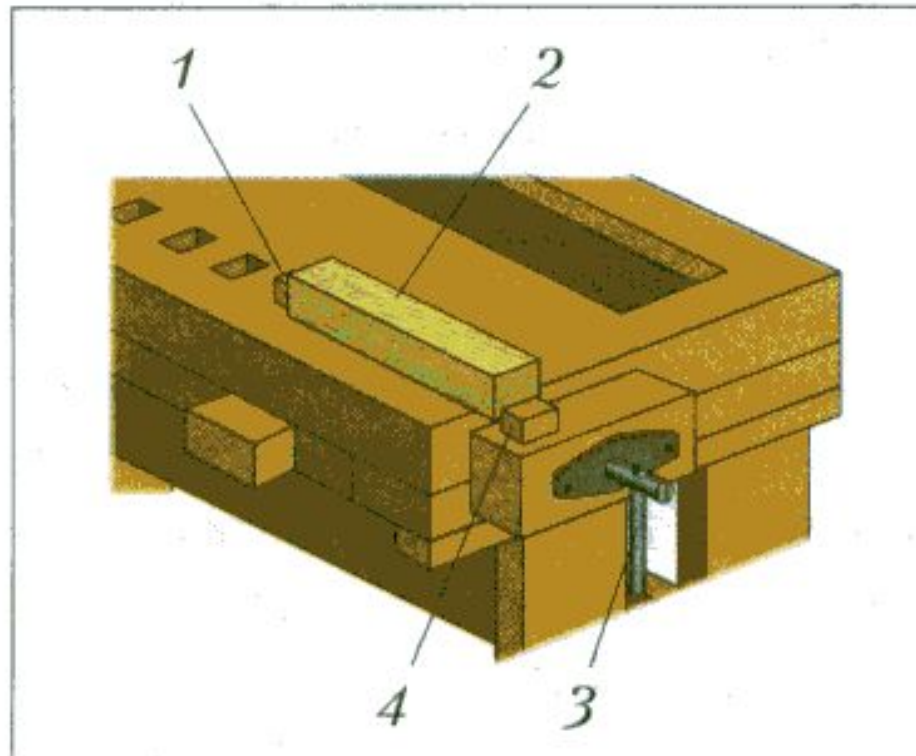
Закрепление заготовки на верстаке: 1 – клин стола; 2 – заготовка; 3 – рукоятка зажима; 4 – клин заднего зажима
